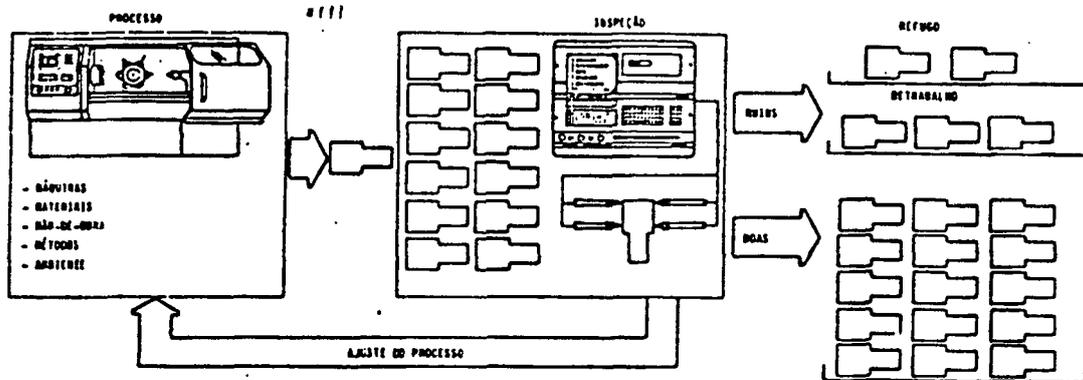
Realimentação do Processo Após a Inspeção Final do Produto
